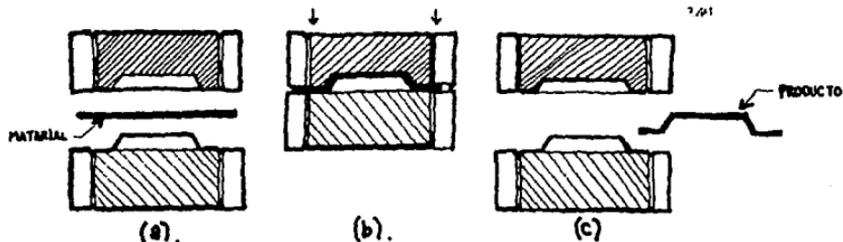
Prensado en caliente con preforma impregnada. Esquema de los pasos de que consta su operación a).- Se deposita la lámina impregnada, b).- Baja la prensa, c).- Se retira la pieza.
